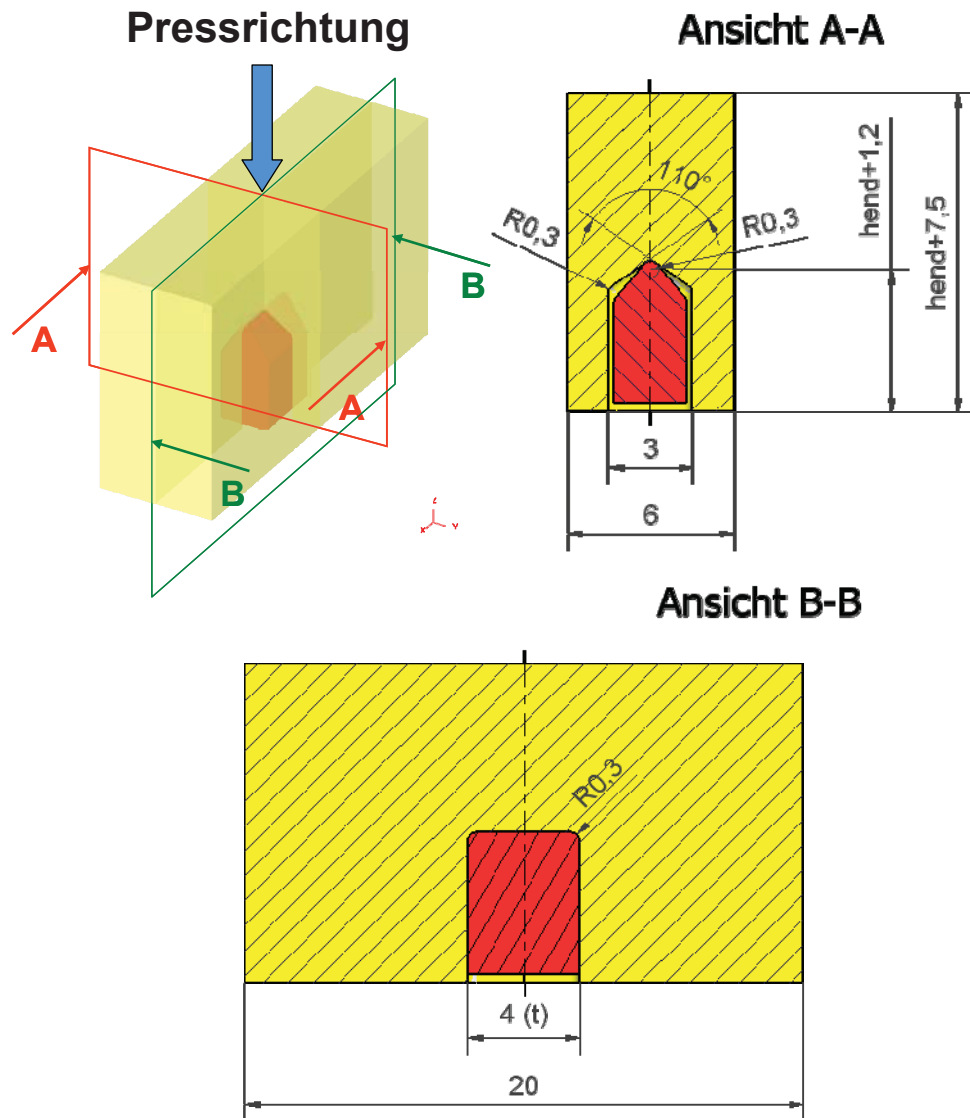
Modell des Verpressens einer beispielhaften Vorform (rot) mit einem axial bewegten Werkzeug (gelb) mit den Hauptabmessungen des Werkzeugs.
